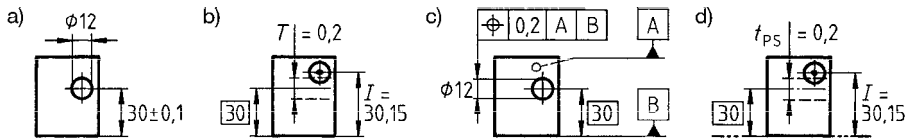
Vergleich von Maß- und Positionstolerierung. a) Maßtolerierung, b) unzulässige Bohrungslage, c) Positionstolerierung entsprechend a, d) entsprechend b
